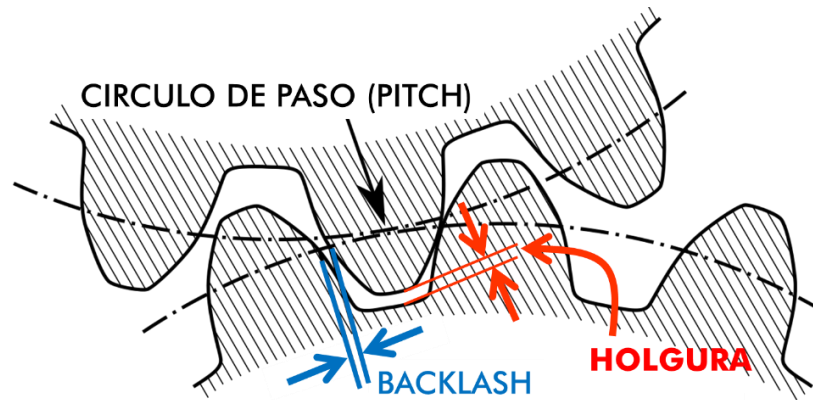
Backlash y holgura en engranajes. Fuente: [23].
